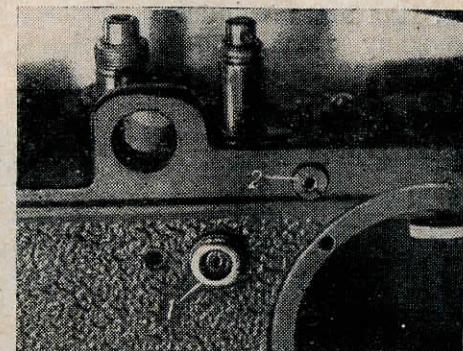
Штуцер крепления пружины и штеккерная розетка
